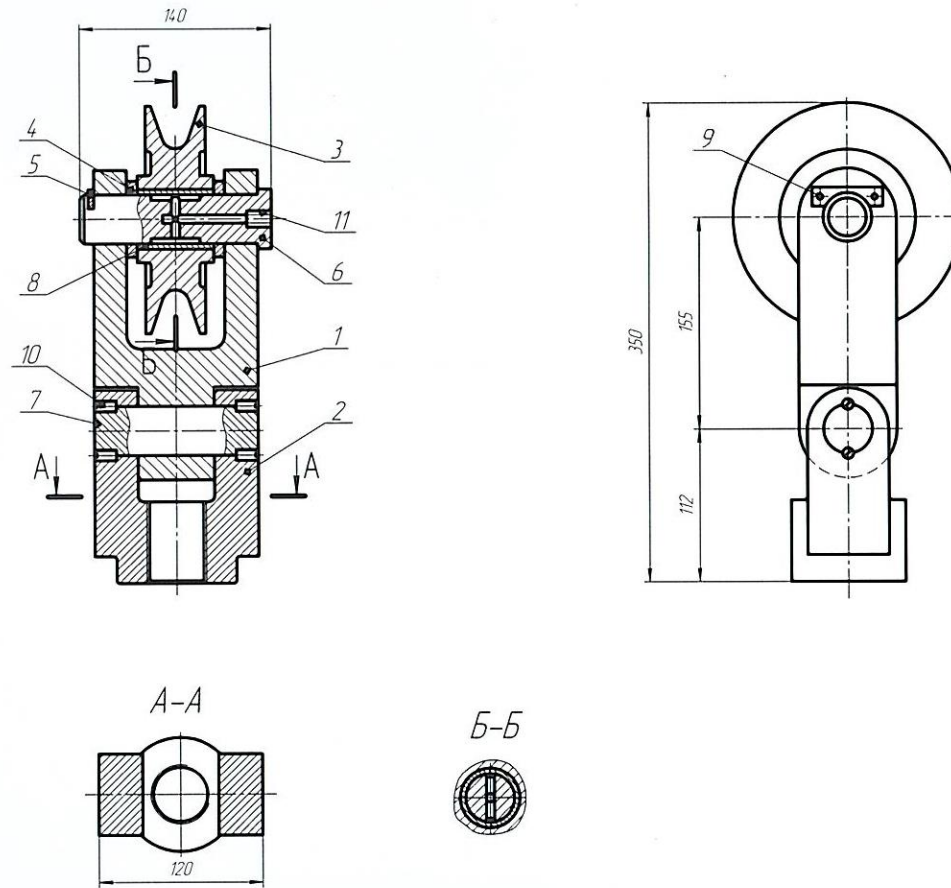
Сборочный чертеж для выполнения листов 7, 8, 9
